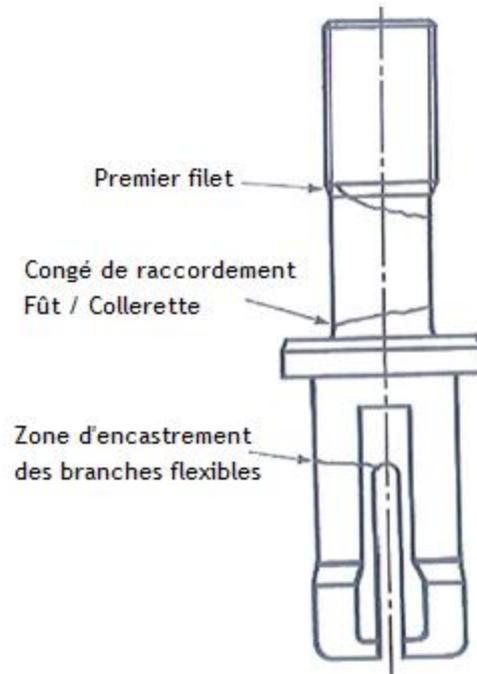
Configurations de fissuration possibles (toutes générations de broche)
